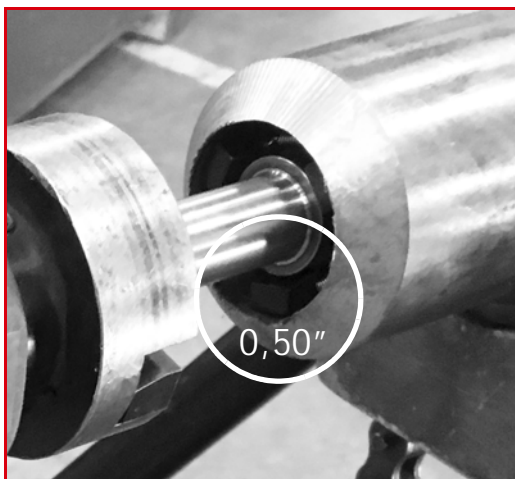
LA BG38 BOILER GUN EN PLACE DANS LA PIÈCE D'USINAGE
